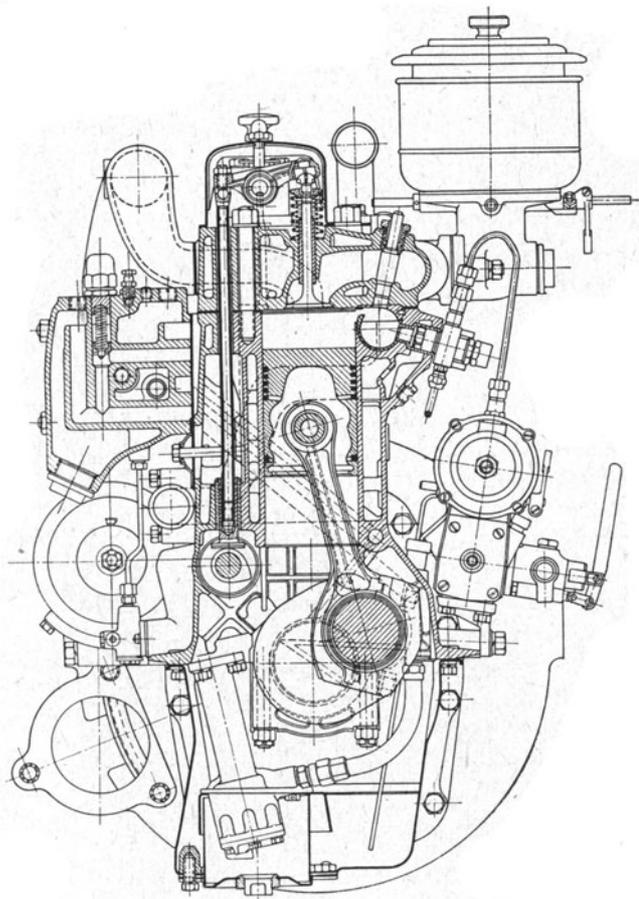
Fahrzeugdieselmotor der Hercules Motor Corporation.
